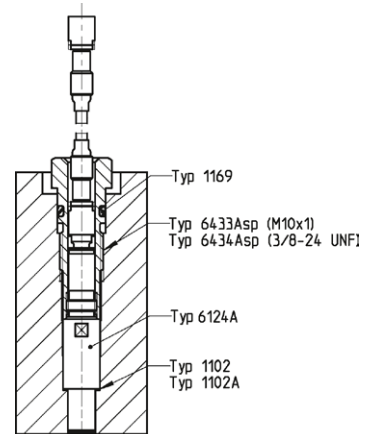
Einbau des Sensors Typ 6124A... mit Montagehülse
